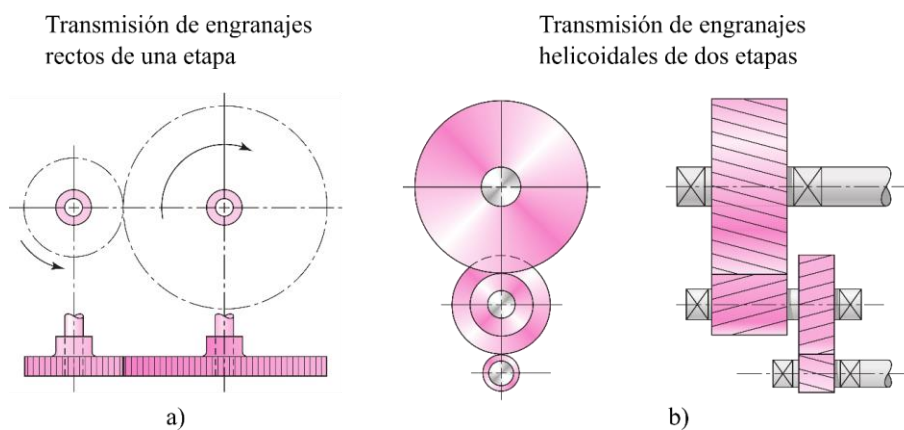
Tipos de transmisiones de engranajes simples [Shigley 2008]: a) engranajes rectos de una etapa, b) engranajes helicoidales de dos etapas.
